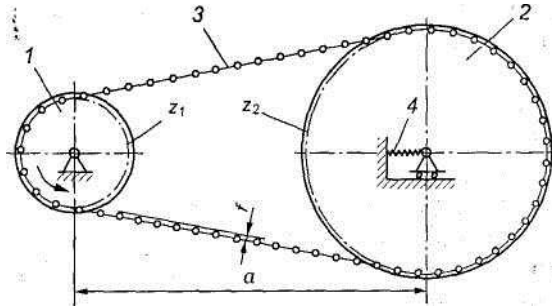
Цепная передача: 1 — ведущая звездочка; 2 — ведомая звездочка; 3 — цепь; 4 — натяжное устройство
